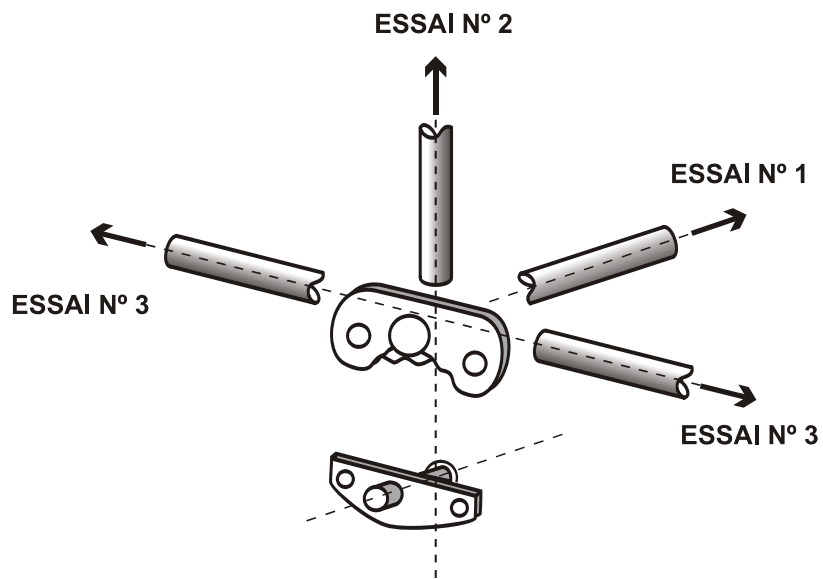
Directions d'application des forces sur le loquet de porte lors de l'essai statique
